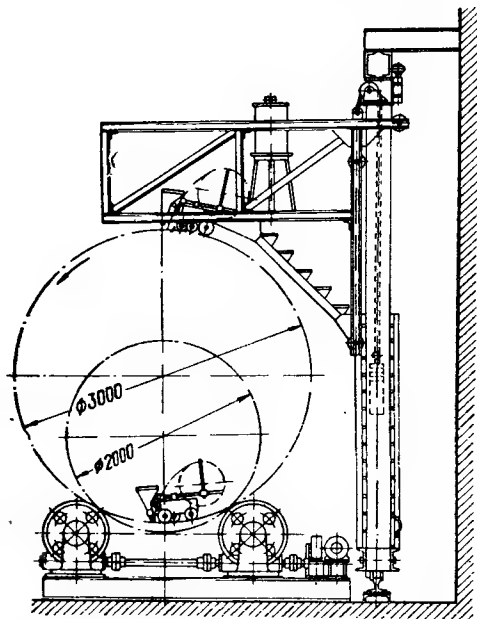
Установка для сварки цилиндрических конструкций трактором
